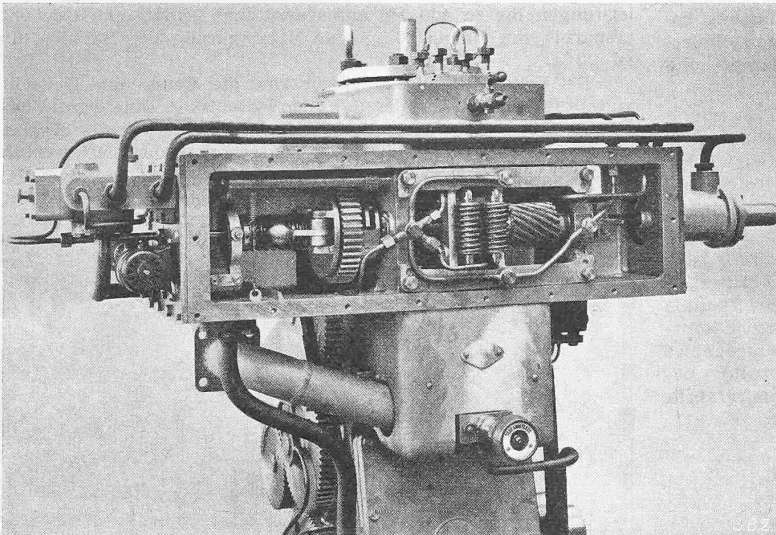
Ansicht des abgedeckten Steuerkastens der SLM-Kolbendampfmaschine
